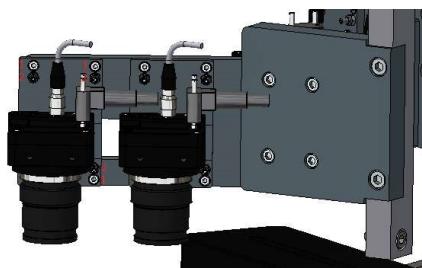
Position des vis de pression et de serrage des caméras au P5P6. 1) Vis de serrage. 2) Vis de pression
